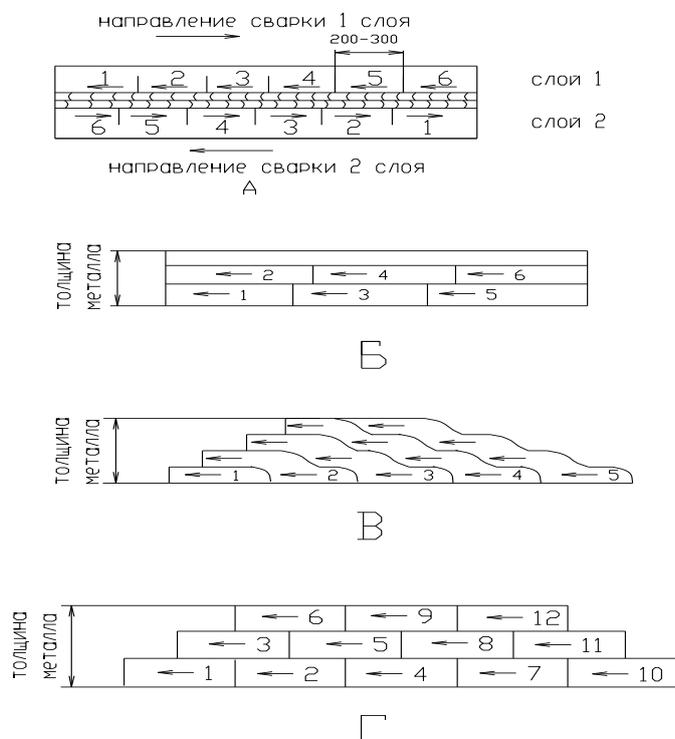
Схемы сварки: обратноступенчатая сварка (а), способом «двойного слоя» (б) сварка каскадом (в, г)
